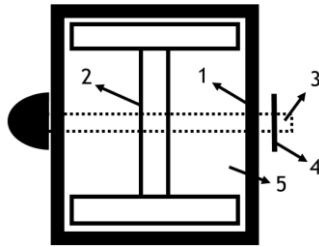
configuração estrutural da ligação entre seções da asa do Crossover
